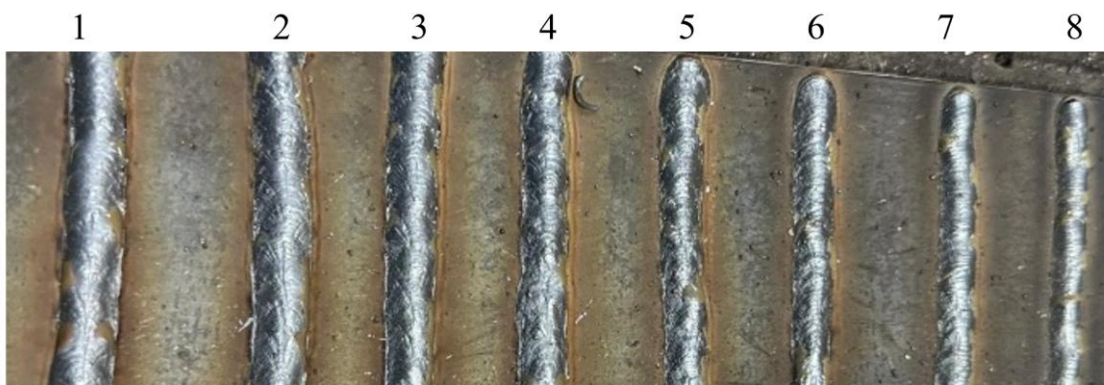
Полуавтоматическая наплавка проволокой марки ОК Tubrodur 35 G M
